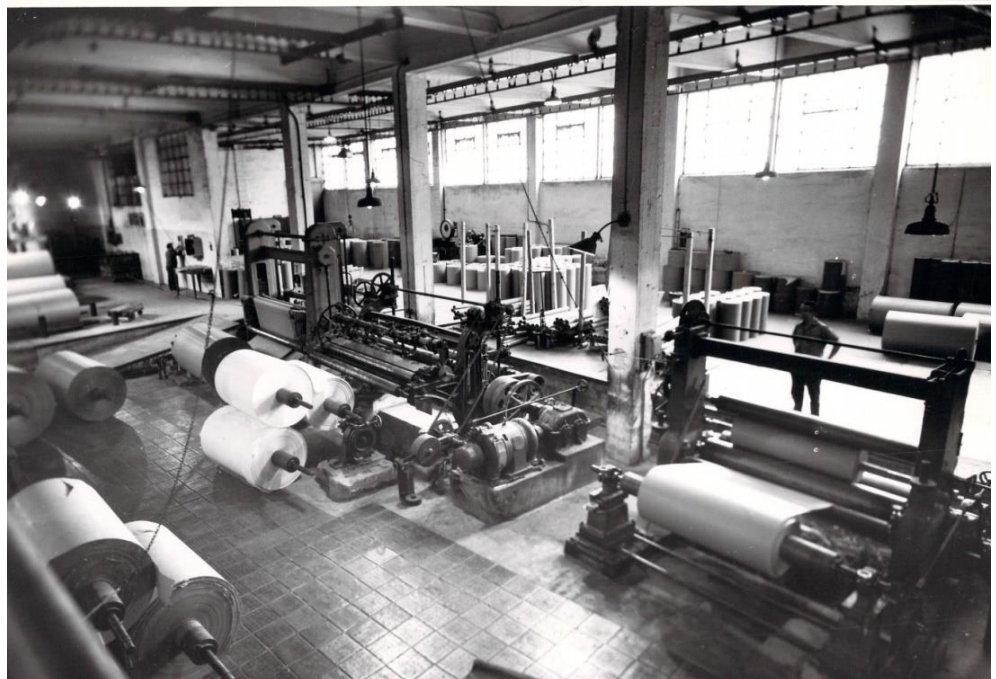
Sección de satinado, en primer plano, y almacén al fondo. (AEPE F 714)
